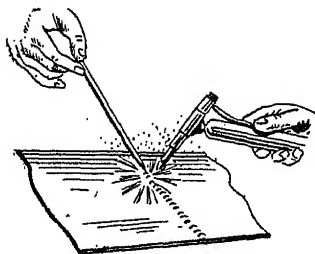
Tenue du métal d'apport et du chalumeau pour la soudure des tôles d'aluminium minces.
